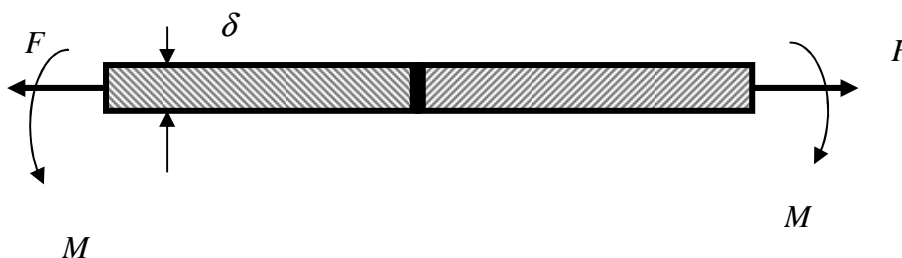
Схема нагружения сварного соединения встык
